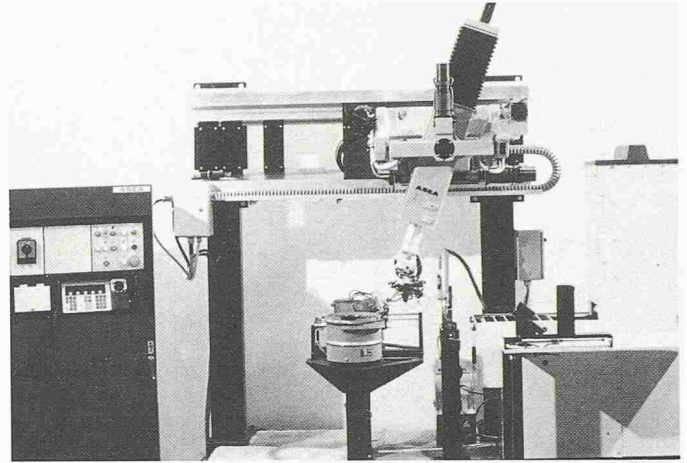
Programmierbare Montagezelle für Anschlussklemmen, mit siebenachsigem Montageroboter mit Bildverarbeitungssystem (Werkbild ASE)
